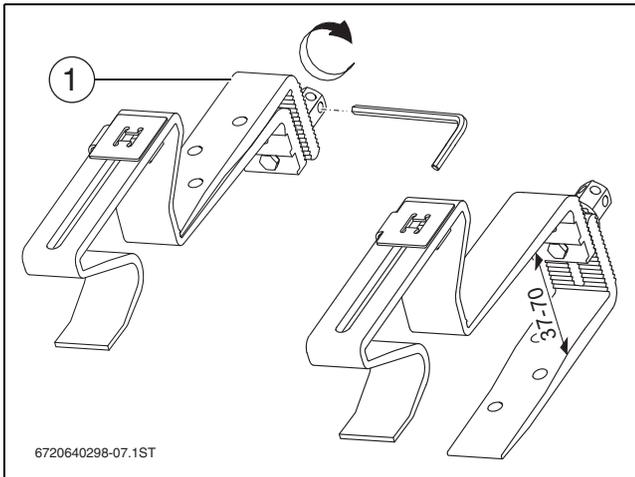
Dachhaken-Unterteil drehen, Maße in mm
